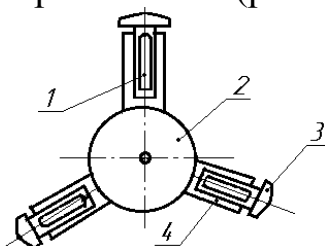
Схема пассивного встряхивателя: 1 – кулачок; 2 – ось; 3 – пластина;
